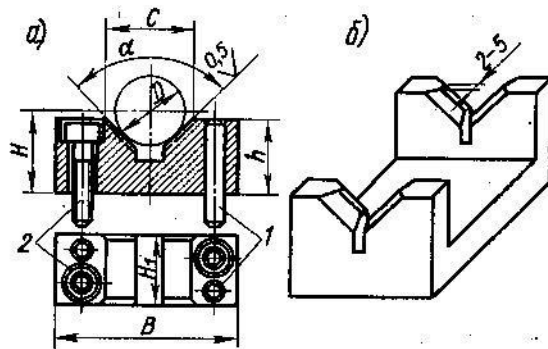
Установочные призмы (а – для установки небольших валов; б – для установки длинных или ступенчатых валов)
